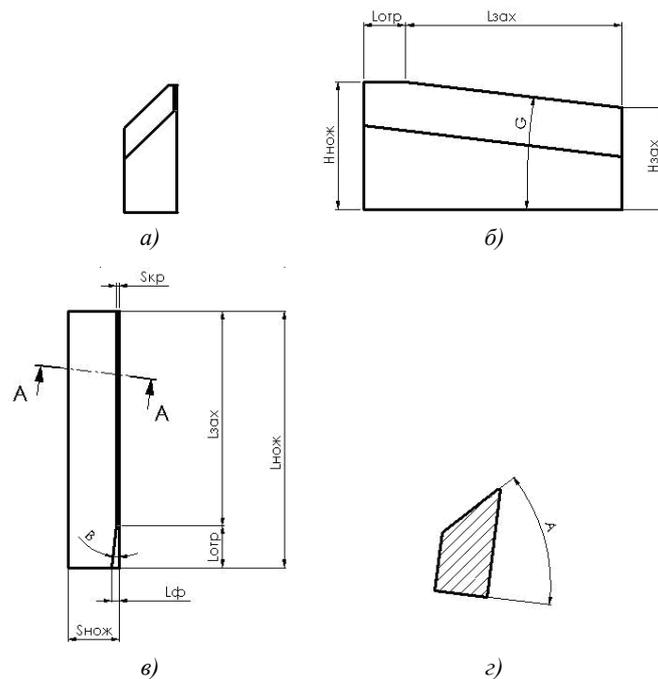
Чертеж отрезного ножа: а) вид спереди; б) вид слева; в) вид сверху; г) сечение А-А
